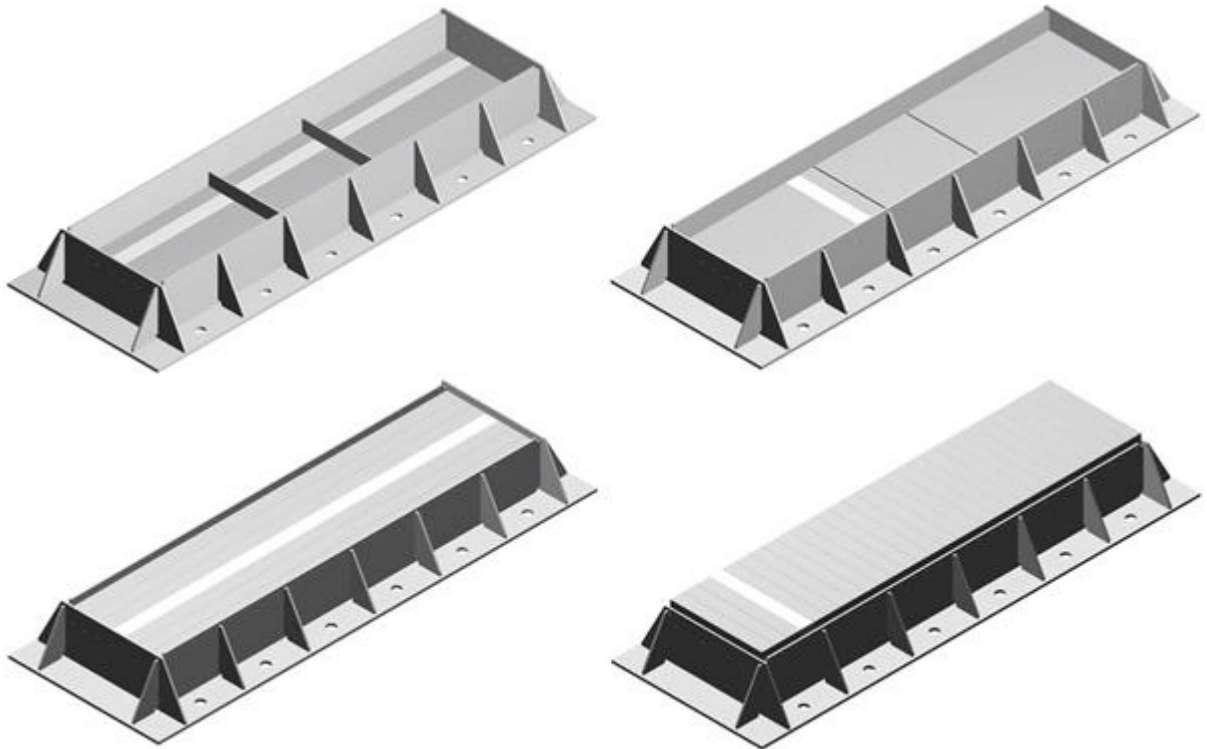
Индентор. Схема укладки деревянных брусьев
